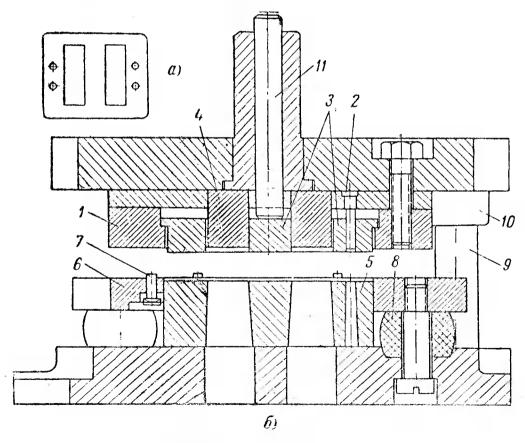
Совмещенный штамп для штамповки пластин трансформатора типа СОБС.
